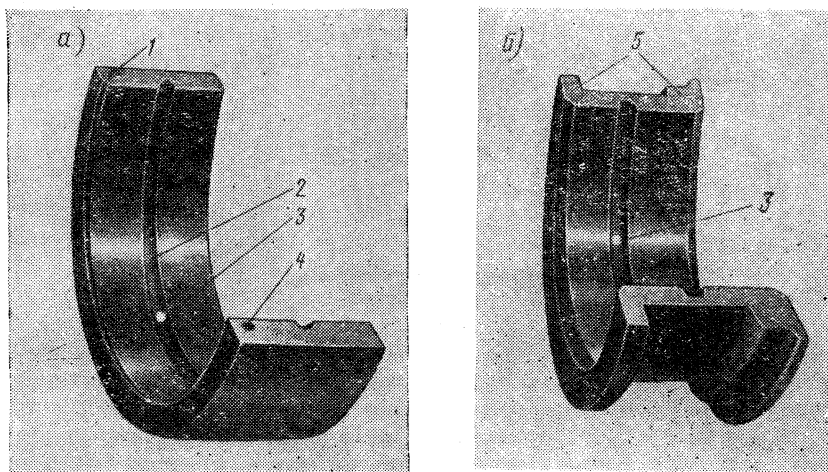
Вкладыши коренных подшипников коленчатых валов дизеля 2Д100:
